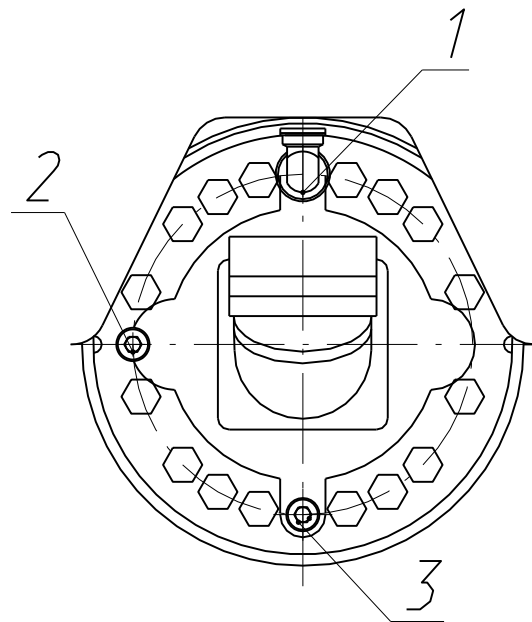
Схема заправки мотор - редуктора привода пневмоколес
